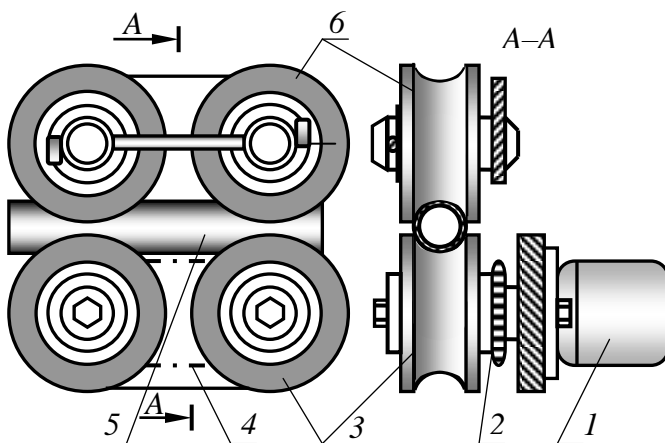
Схема механизма для перемещения напорного шланга.
